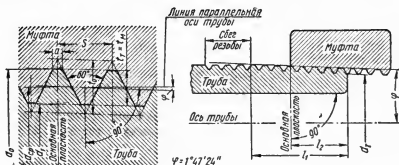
Профиль конической дюймовой резьбы по ГОСТ 6111—52.
